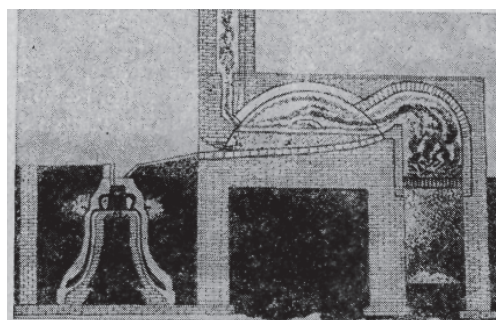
Схема пламенной печи для плавки бронзы, подвода металла к литейной форме с заформованным в ней колоколом
